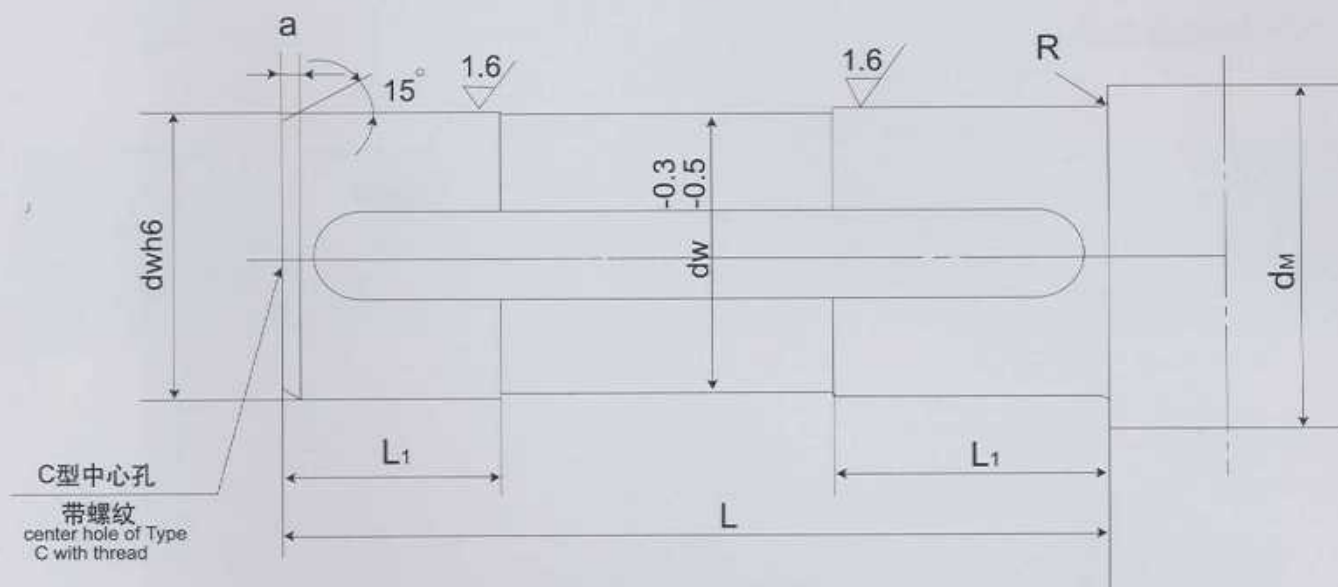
平键联接的轴 Figure 11 Flat key connecting axle
